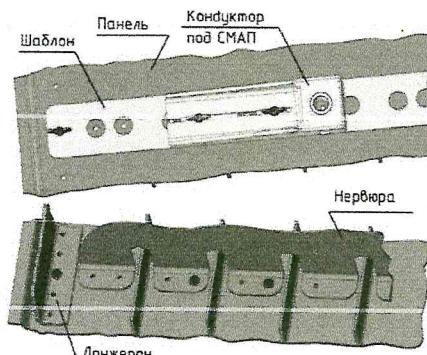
Кондуктор для сверления отверстий по нервюрам
